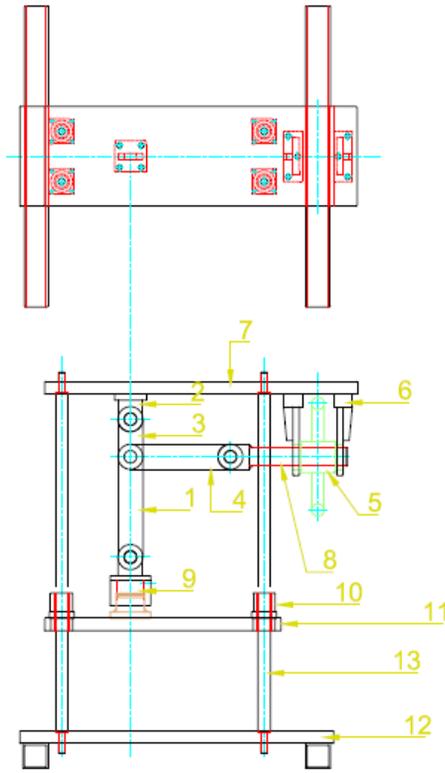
Dibujo de armado de la Prensa y las partes que la componen.
